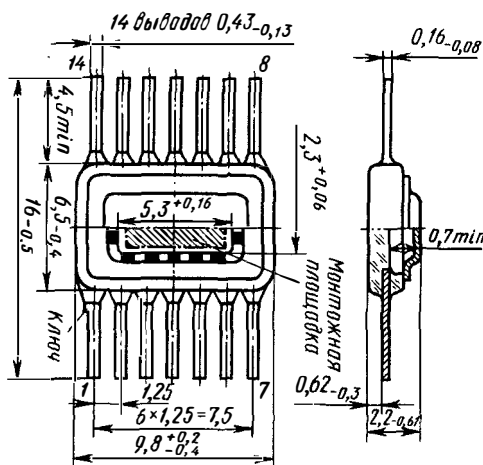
Металлостеклянный корпус типа 4105 (401.14-3)
